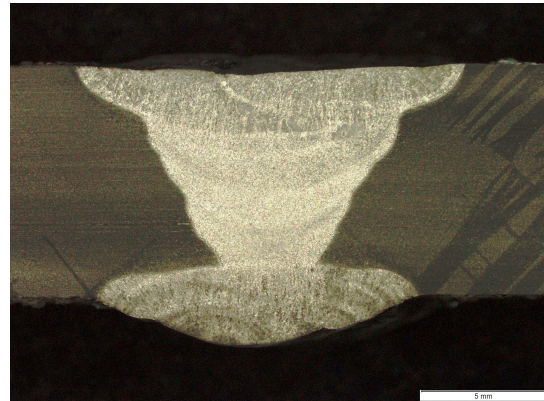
Probe G04-04, Schweißnaht FAT 90, Riss neben der Schweißnaht, Nahtansatzwinkel
